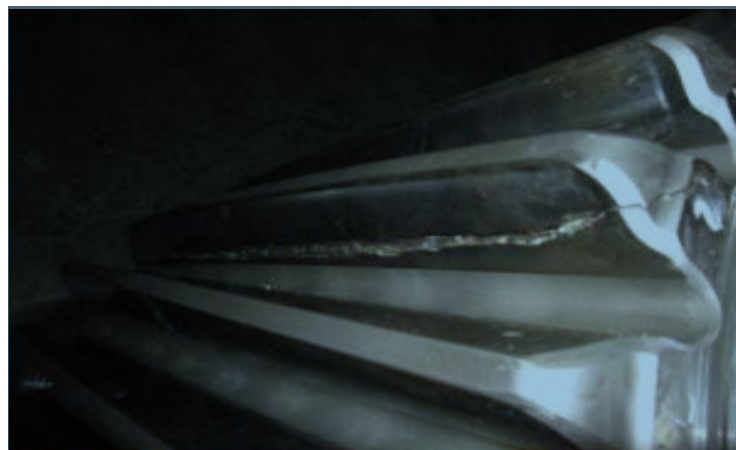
Fissuration ou cracks "Engrenages" Écaillage.
